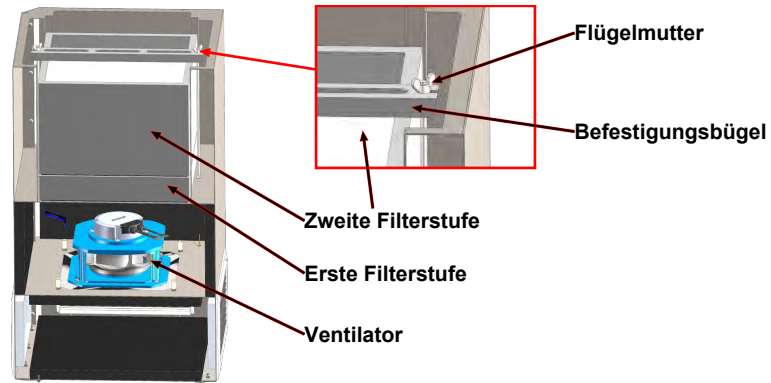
Schnittansicht zur Befestigung der Filterelemente
